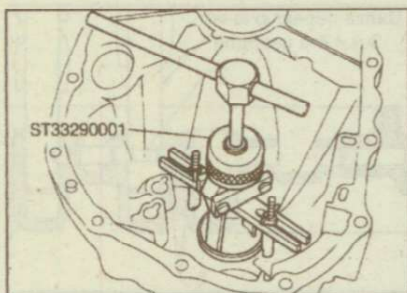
Снятие наружного кольца подшипника вторичного вала
